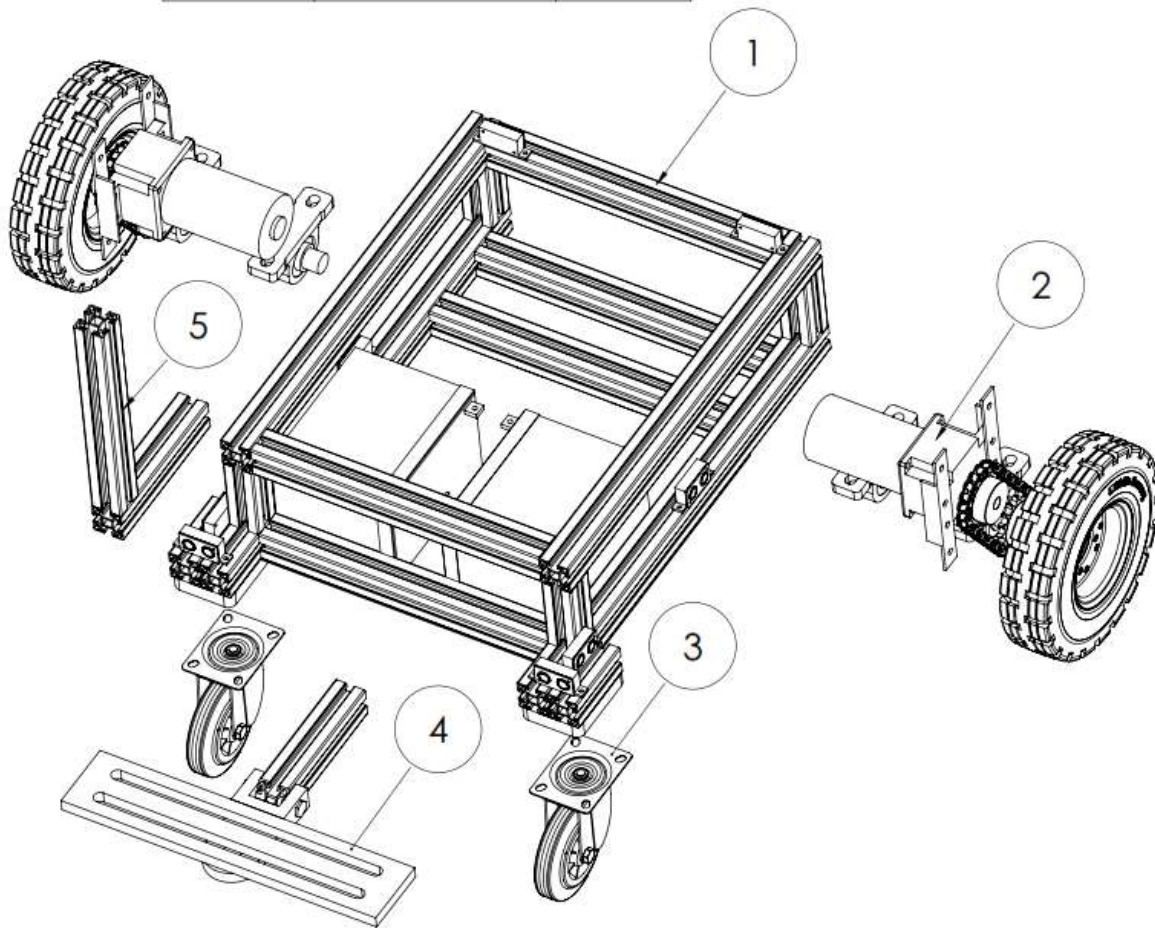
Diagrama explosionado y elementos que componen al chasis de la SRM.
